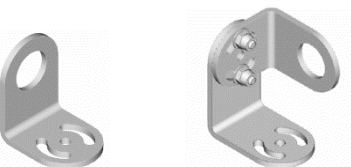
starrer und justierbarer Montagewinkel
